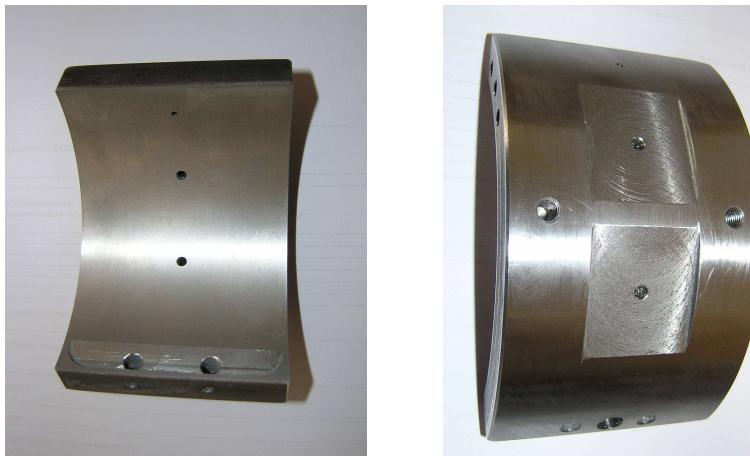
Реверсивные опорные колодки с нереверсивными свойствами.
